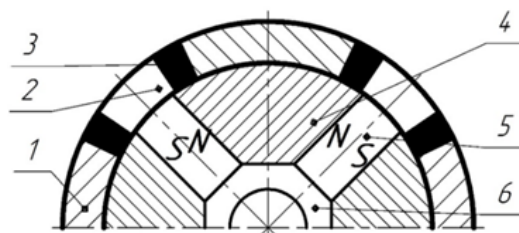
Ротор с призматическими магнитами, имеющими тангенциальное намагничивание: 1 – полюсные наконечники; 2 – немагнитные участки обода; 3 – сварной шов; 4 – полюсы; 5 – магнит; 6 – немагнитная втулка
